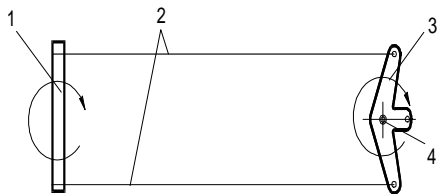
Схема передачі механічного руху з ручки корду на борт моделі: 1 – ручка корду; 2 – нитки корту; 3 – гойдалка (встановлюється на борту моделі); 4 – вісь обертання гойдалки
